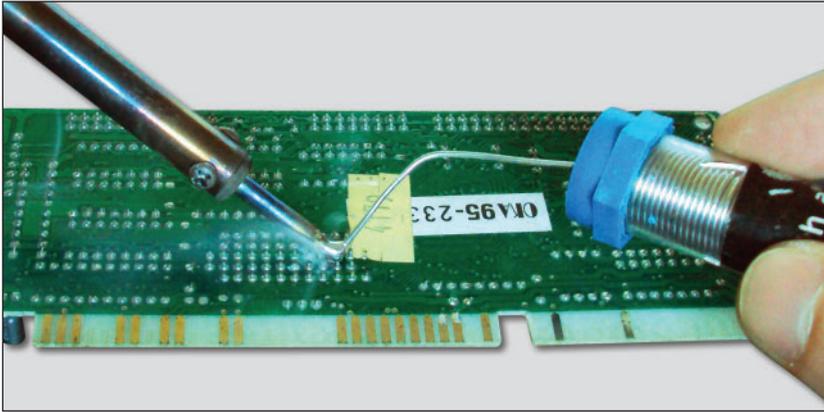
Típico soldador de estaño aplicando una soldadura sobre una placa. Es una herramienta muy económica de uso casi imprescindible.
